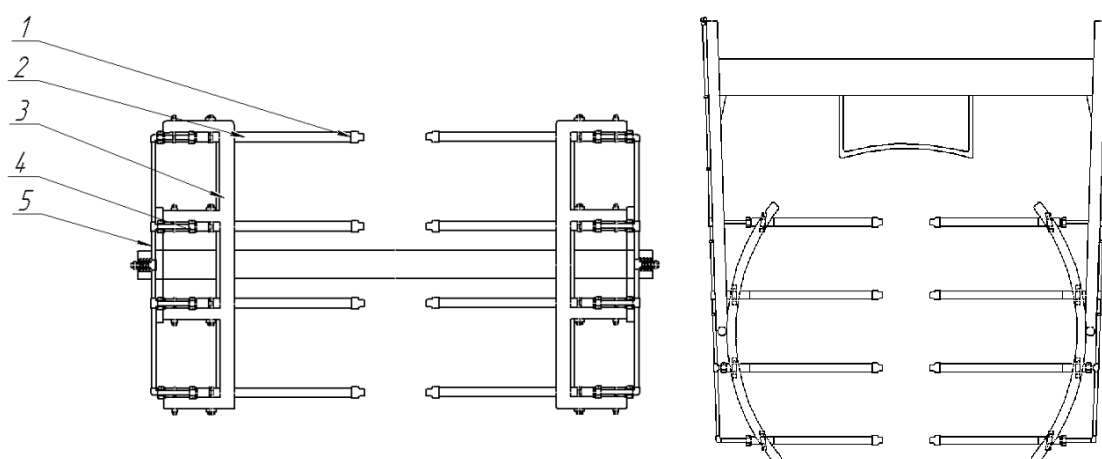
Схема приспособления для обработки жидкими химическими консервантами прессованных рулонов сенажа:
